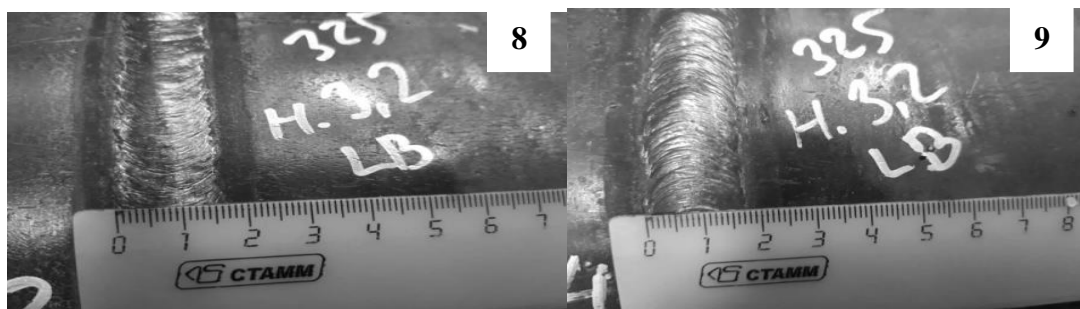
Сварное соединение 8. Рисунок Б29. Сварное соединение 9.
